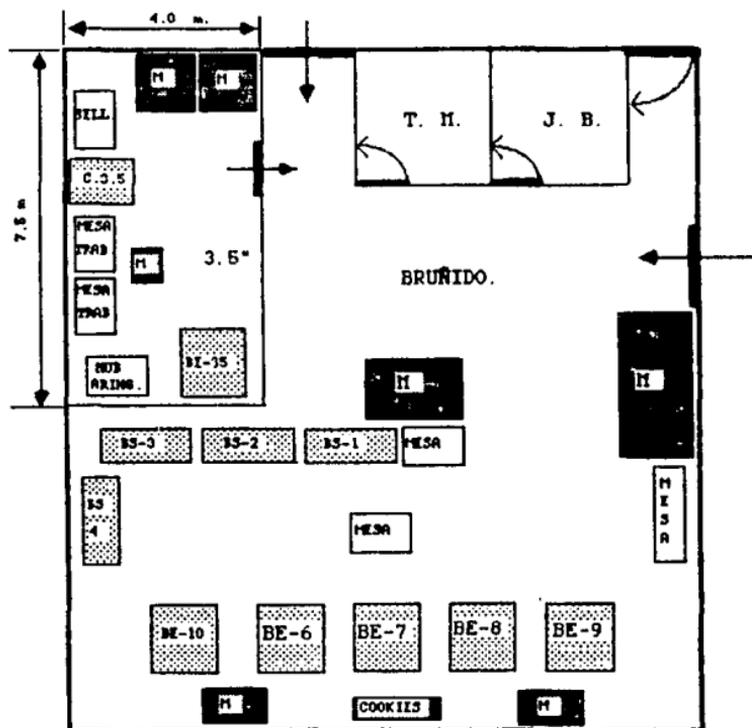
LAY-OUT ACTUAL LINEA DE ENSAMBLE DE DISKETTES DE 3.5".
